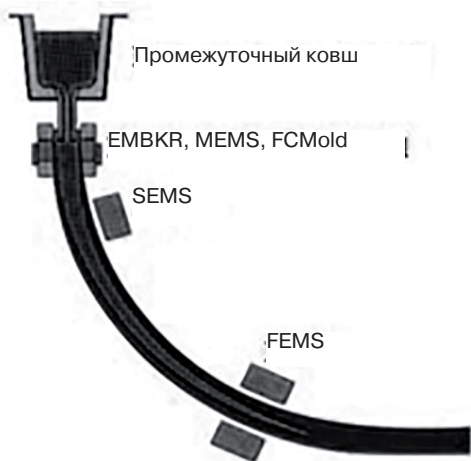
Электромагнитные воздействия при формировании непрерывнолитой заготовки
